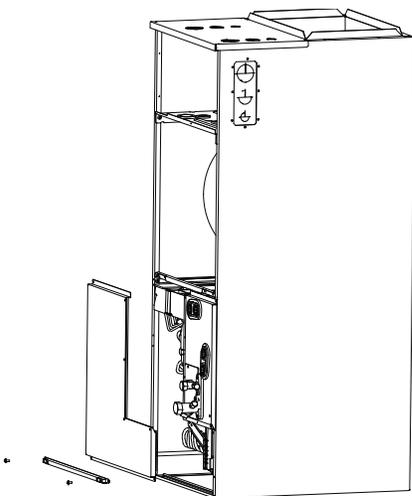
Réinstallez la plaque de protection de l'évaporateur.
